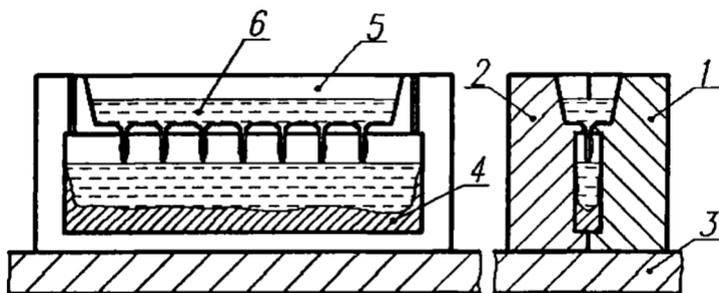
Схема получения заготовок цинковых анодов литьем в кокиль: 1 – полуформа подвижная; 2 – полуформа неподвижная; 3 – плита; 4 – отливка; 5 – литниковая система; 6 – жидкий металл
